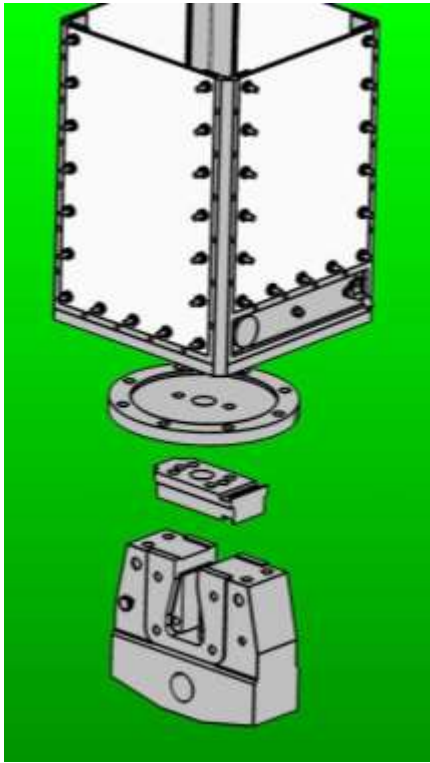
Representación del montaje y la disposición de las piezas involucradas.
